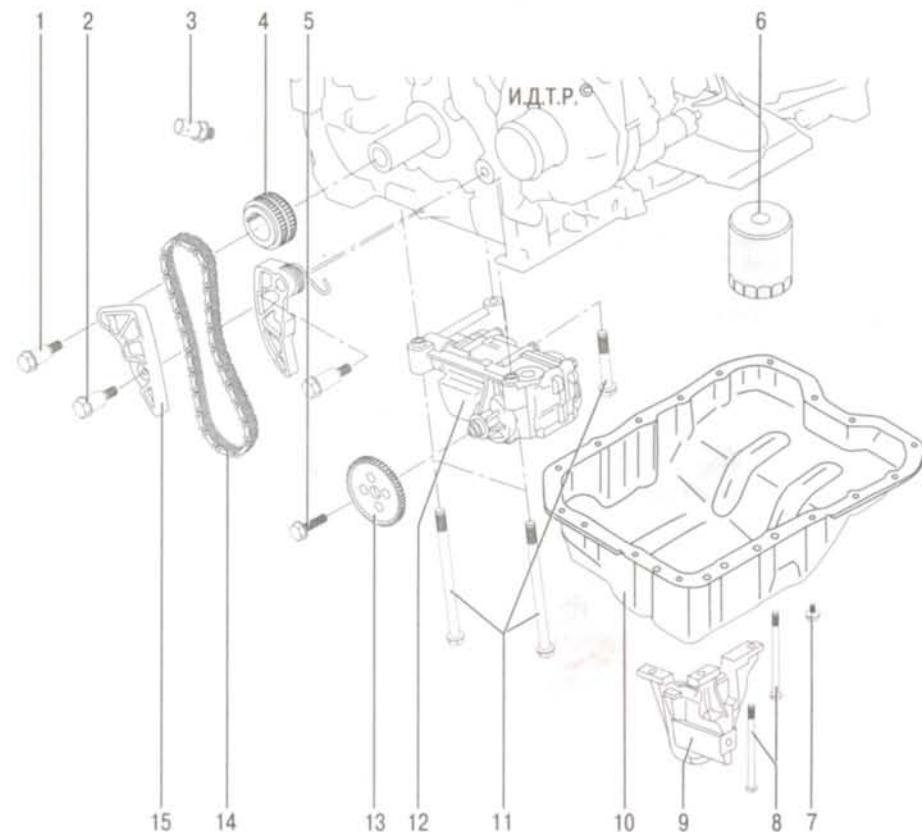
Детали системы смазки: 1 – болт крепления успокоителя цепи; 2 – регулировочный болт успокоителя цепи; 3 – датчик давления масла; 4 – звездочка привода газораспределительного механизма и привода масляного насоса; 5 – натяжитель цепи; 6 – масляный фильтр; 7 – пробка поддона картера; 8 – болты крепления кронштейна компрессора кондиционера; 9 – кронштейн крепления компрессора кондиционера; 10 – масляный картер; 11 – болты крепления масляного насоса; 12 – масляный насос; 13 – звездочка масляного насоса; 14 – цепь привода масляного насоса; 15 – успокоитель цепи
